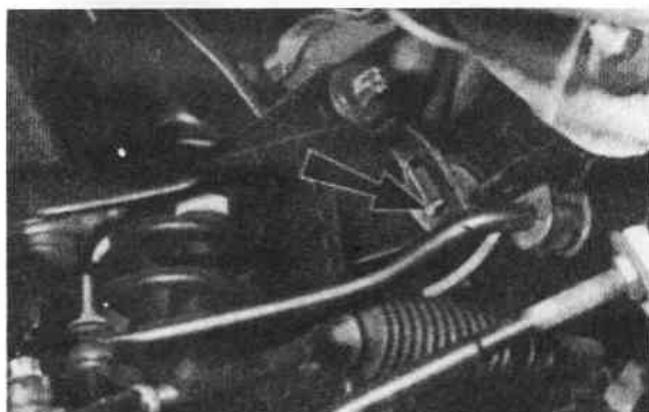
Шпилька крепления двигателя (гайка удалена) (Разд.5)
